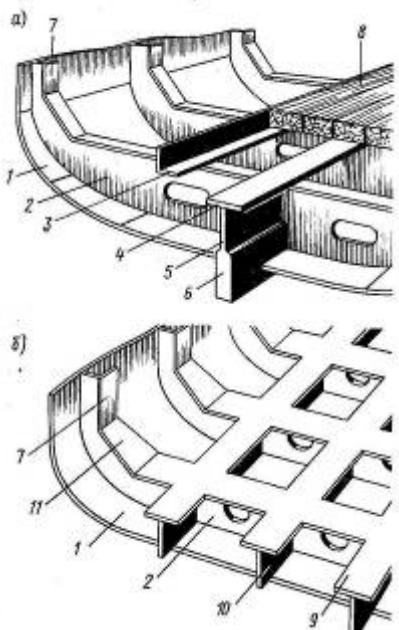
Одинарное дно: а - средний кильсон; б - средний кильсон в виде сплошного среднего килевого листа. 1- наружная обшивка; 2- флор; 3 - стрингерный угольник; 4 - поясок кильсона; 5 - средний килевой лист; 6 - брусковый киль; 7 - шпангоут; 8 - деревянный настил; 9- средний кильсон; 10- боковой кильсон; 11 - скуловая кница
